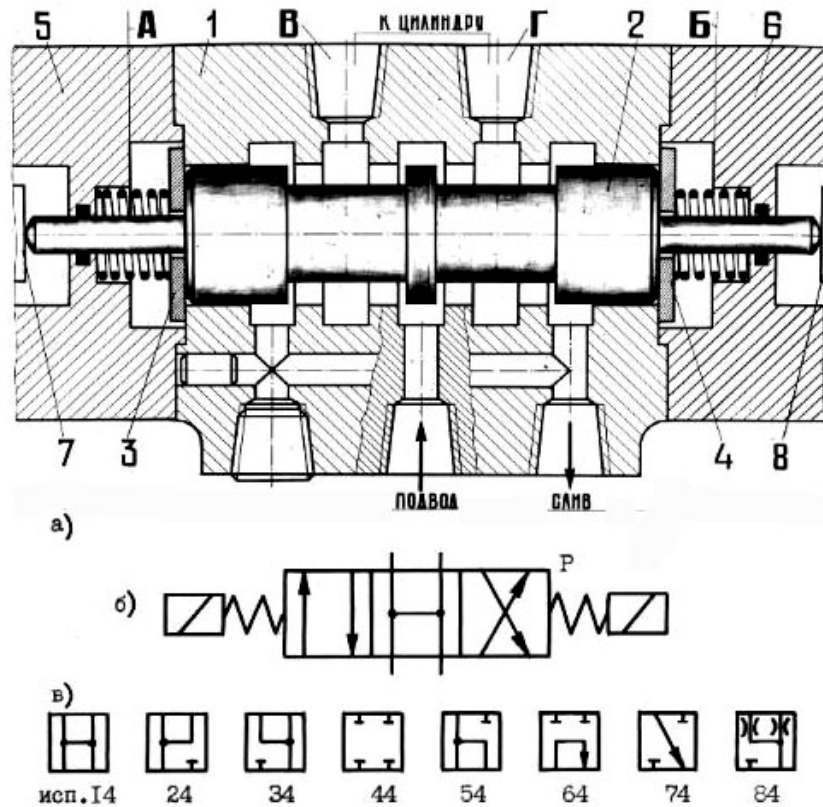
Четырехлинейные трехпозиционные гидрораспределители: а, б - конструктивная схема /а/ и условное обозначение /б/ распределителя с электромагнитным управлением: 1 - корпус; 2 - цилиндрический золотник или плунжер; 3, 4 - шайбы; 5, 6 - фланцы; 7, 8 - электромагниты; в - варианты некоторых исполнений распределителей по гидросхеме /средняя позиция/
